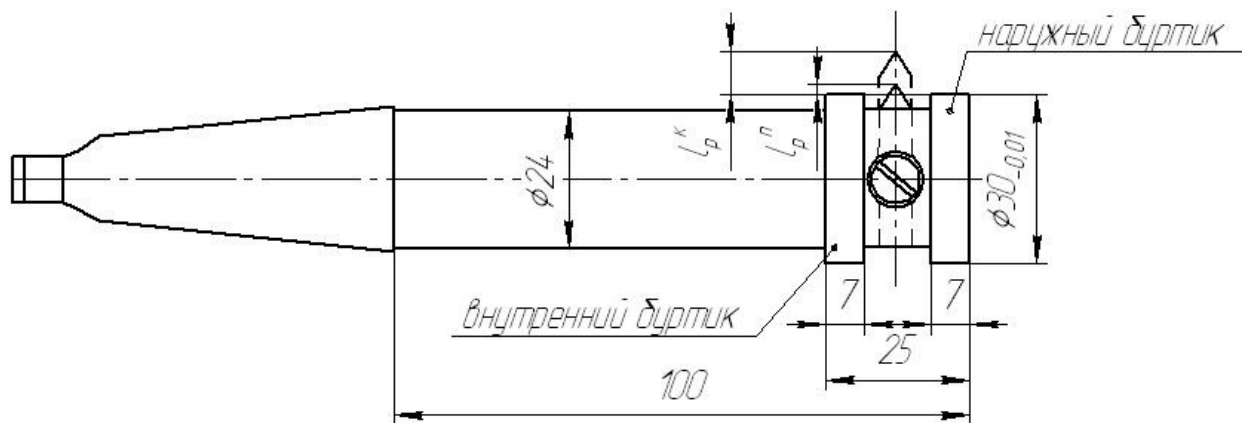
Расточная головка для обработки полуотверстий и колодцев поджимной полуобоймы
